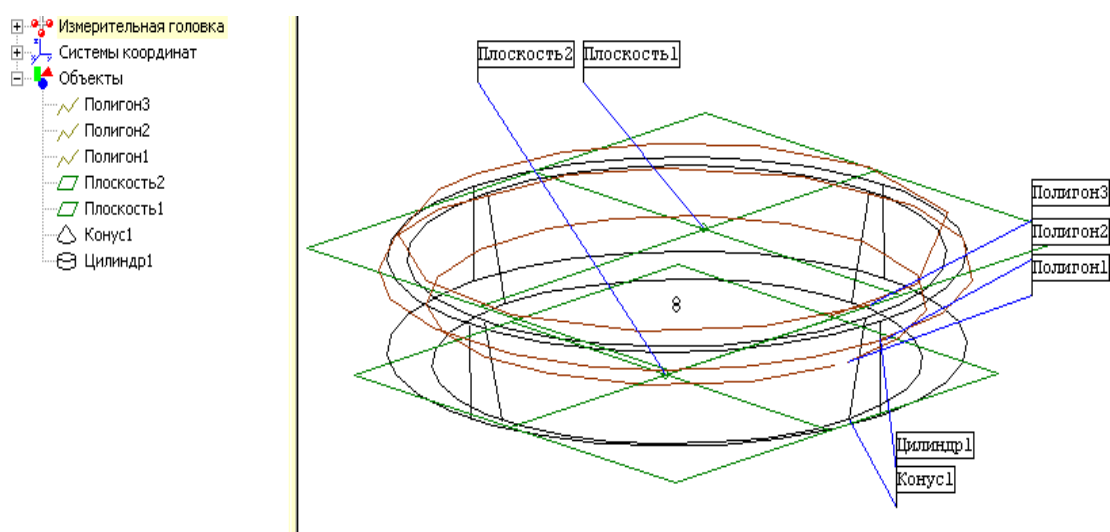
Сеанс вимірювання кільця роликового підшипника
